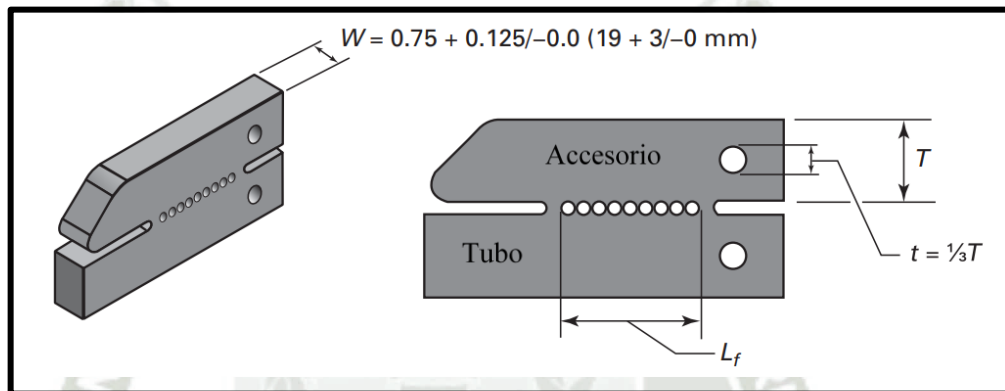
Dimensiones del espécimen para el ensayo de Peel test.
